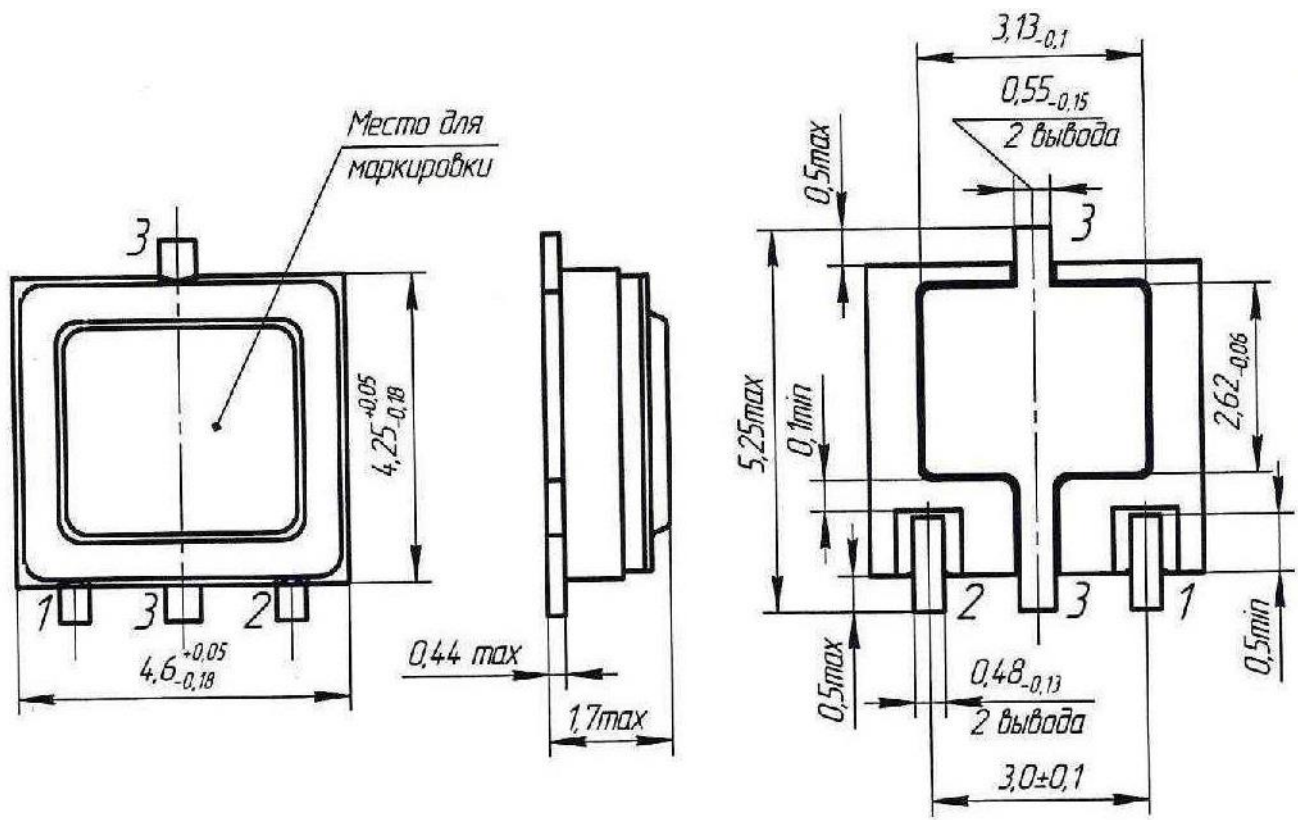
Габаритный чертеж корпуса КТ-97В-22.01
